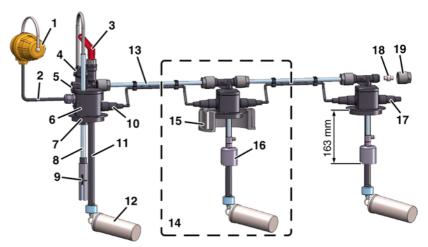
Grundeinheit mit GWG 12 K/1R-SWS und Erweiterung mit Schwimmerschalter
